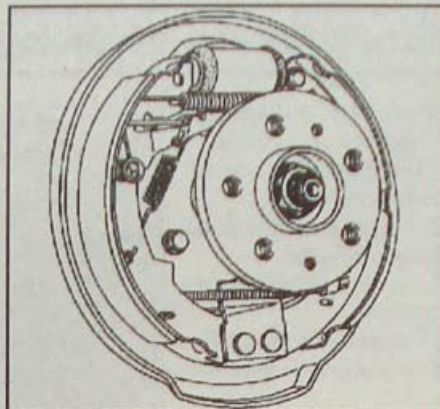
Расположение гайки крепления ступицы заднего колеса
